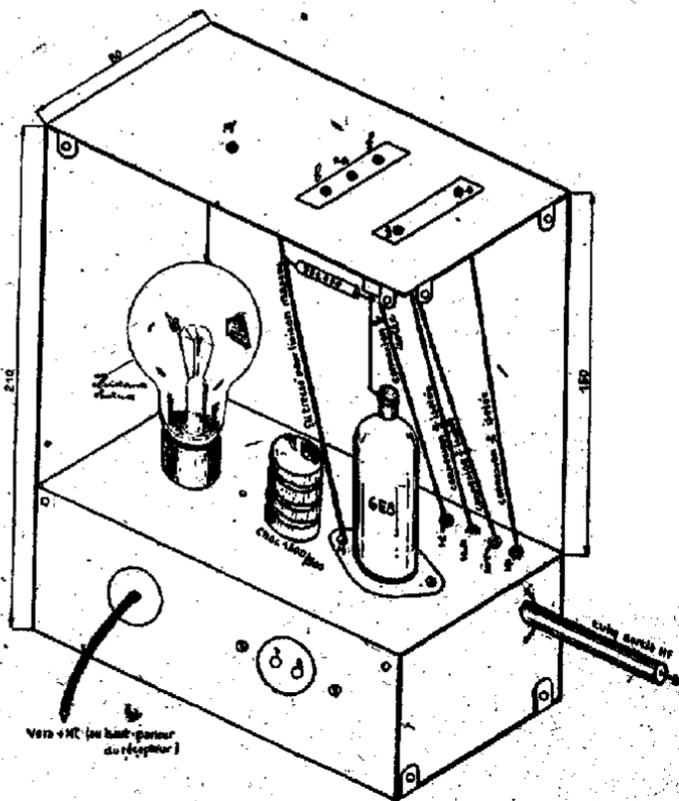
Vue en perspective du bloc vu de l'arrière, le flanc et la plaque arrière étant enlevés.
